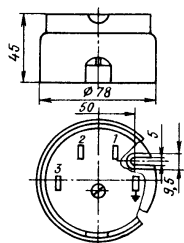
Габаритные, установочные размеры вилки круглой формы
